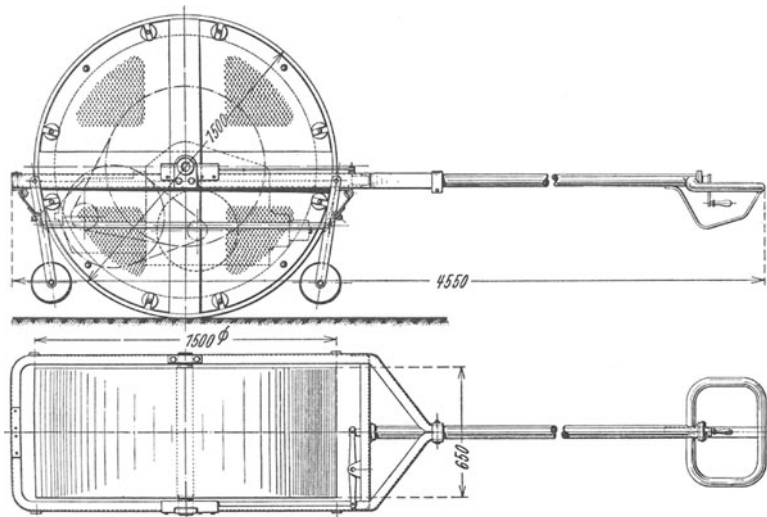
Einradwalze der Berliner Maschinenbau A.-G. Schwartzkopff.
